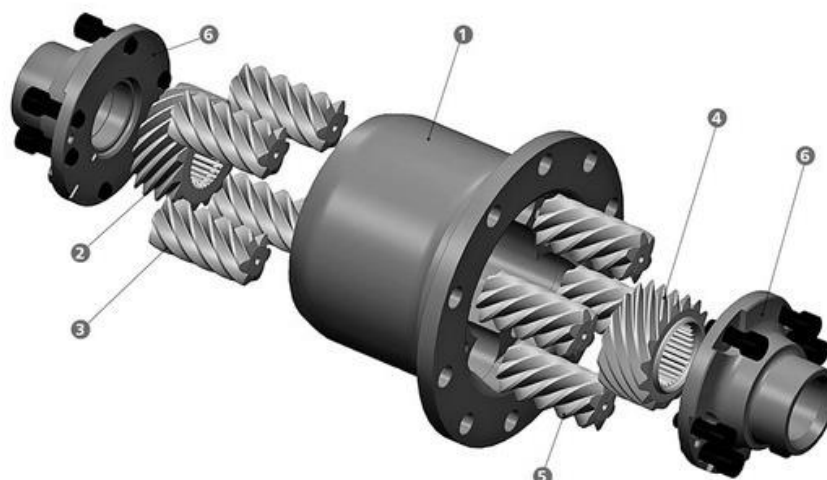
Дифференциал Torsen T-1: 1-корпус; 2-левая полуосевая шестерня; 3-пара червячных сателлитов; 4 - правая полуосевая шестерня; 5-ось сателлитов; 6-прямозубые шестерни взаимного зацепления сателлитов
